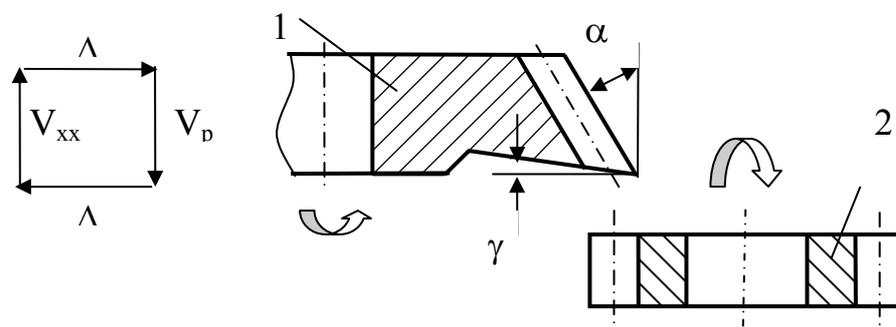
Схема нарезания зубчатого колеса долбяком:
